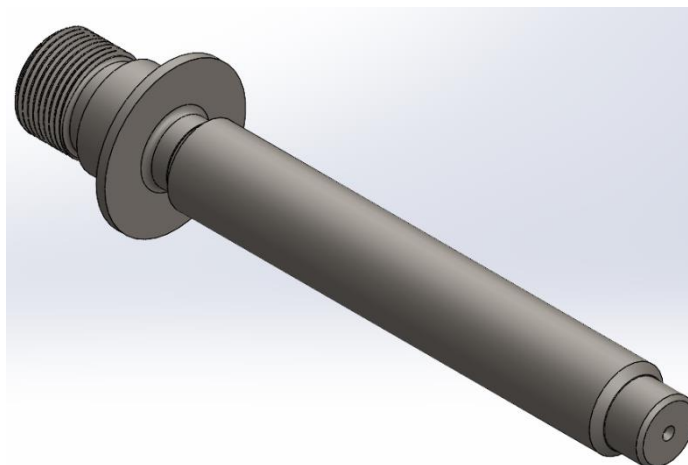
Заготовка для обробки деталі на операції 050
